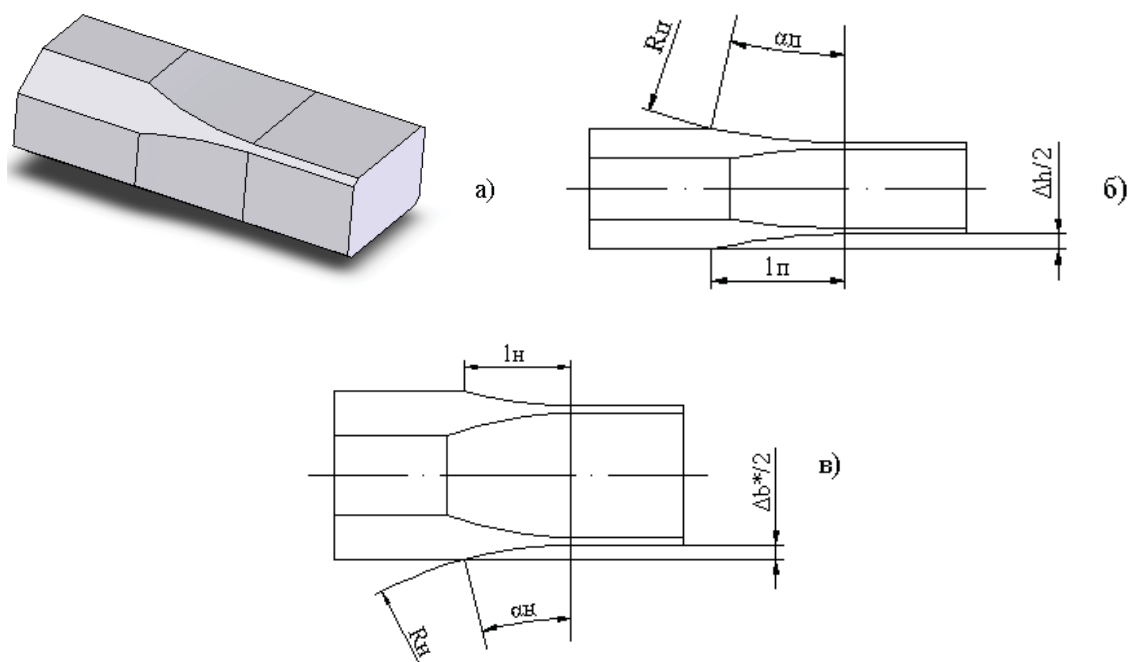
Четырехвалковый очаг деформации с примыкающими внешними зонами: а) общий вид; б) вид со стороны неприводного валка; в) вид со стороны приводного валка
